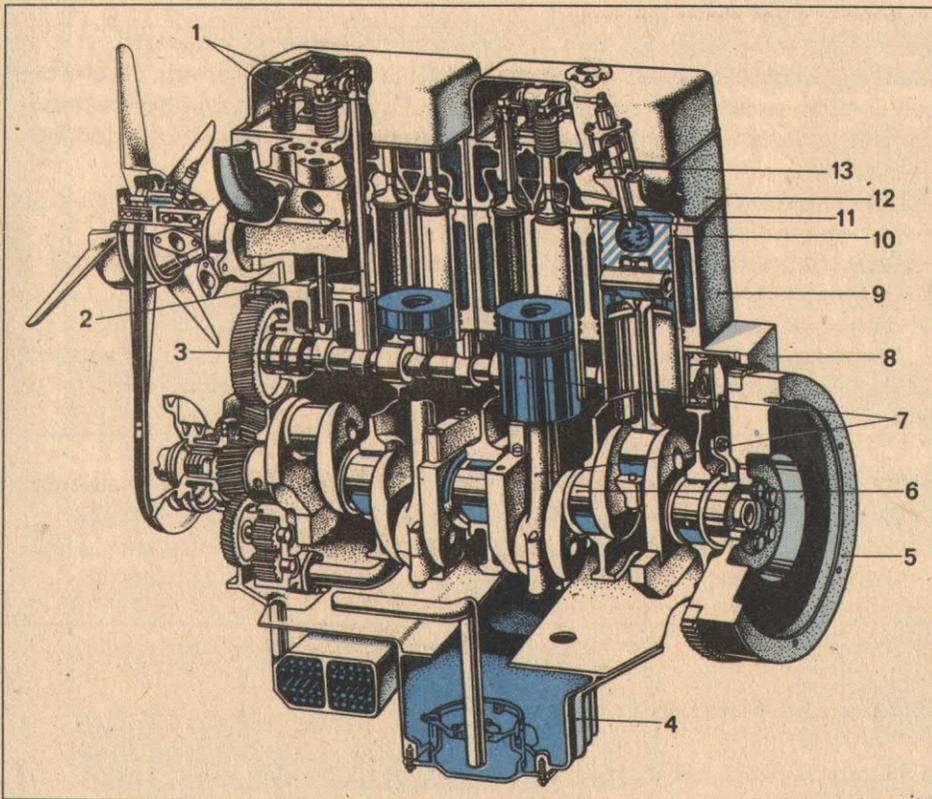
/1 Vierzylinder — Viertakt — Dieselmotor (Schnittdarstellung)
